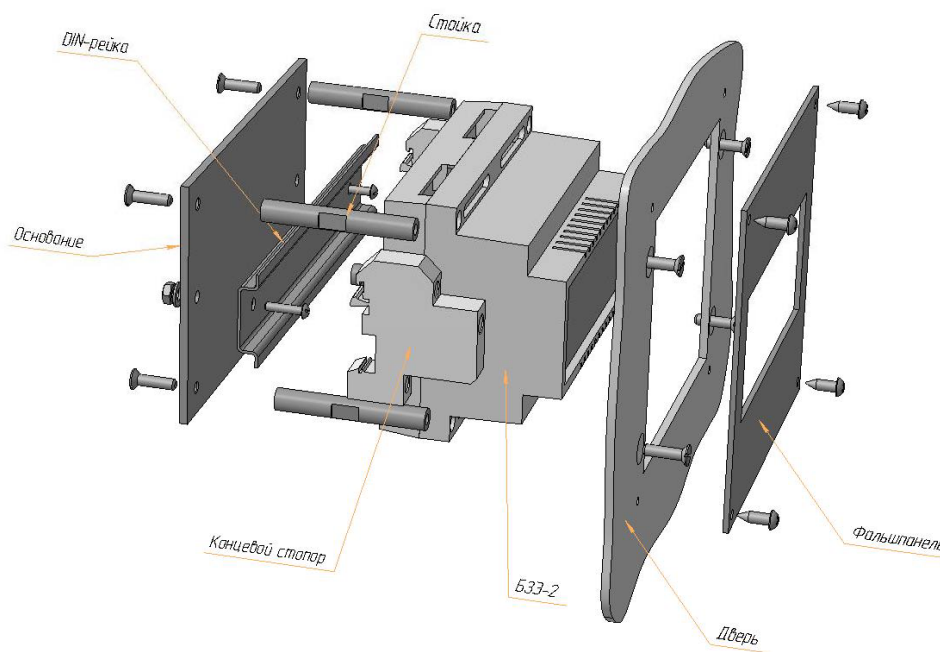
Схема установки БЗЭ-2 на двери шкафа
